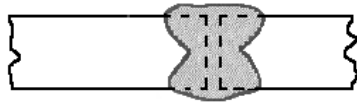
Con extremos planos, soldadura por ambos lados de la junta.
